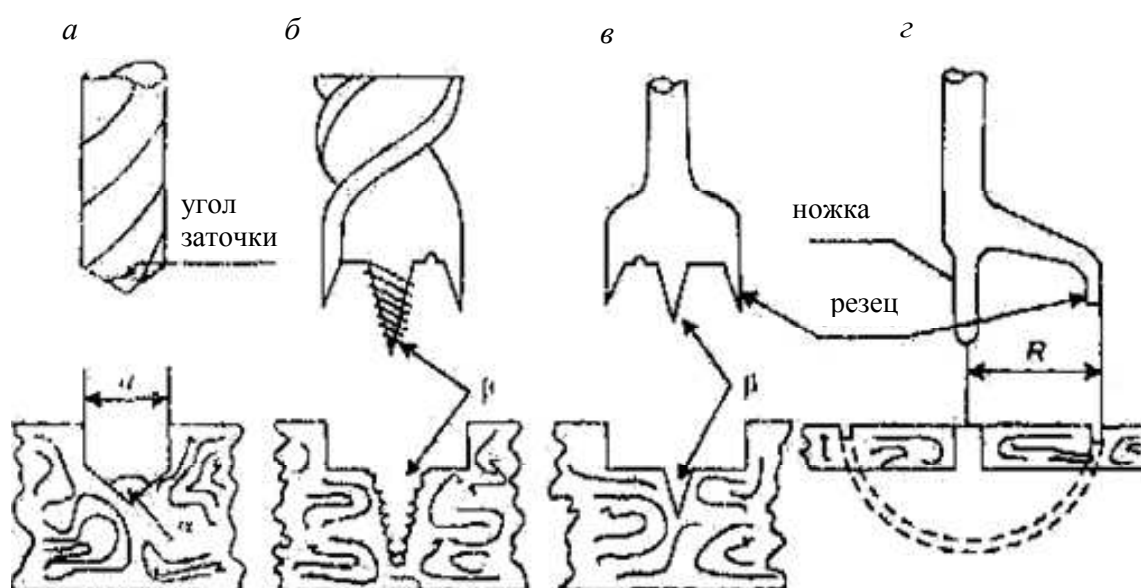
Схематический вид инструментов для сверления и вид следов, оставаемых ими: а – сверло из металла, б – центровое сверло «центровка», в – перьевое сверло – «перка», г – «балерина»
